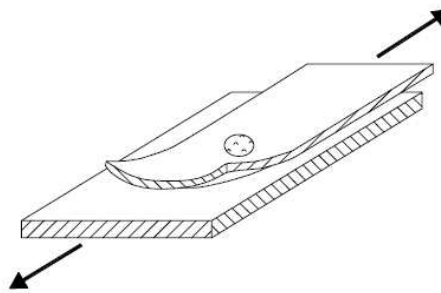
Soldaduras de muesca y de tapón [3]
